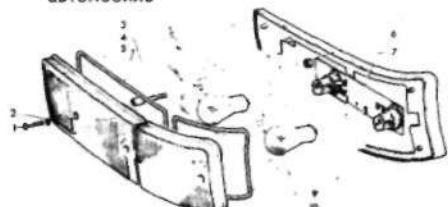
Установка парковочного фонаря и указателя поворота — сзади (Раздел 26)
